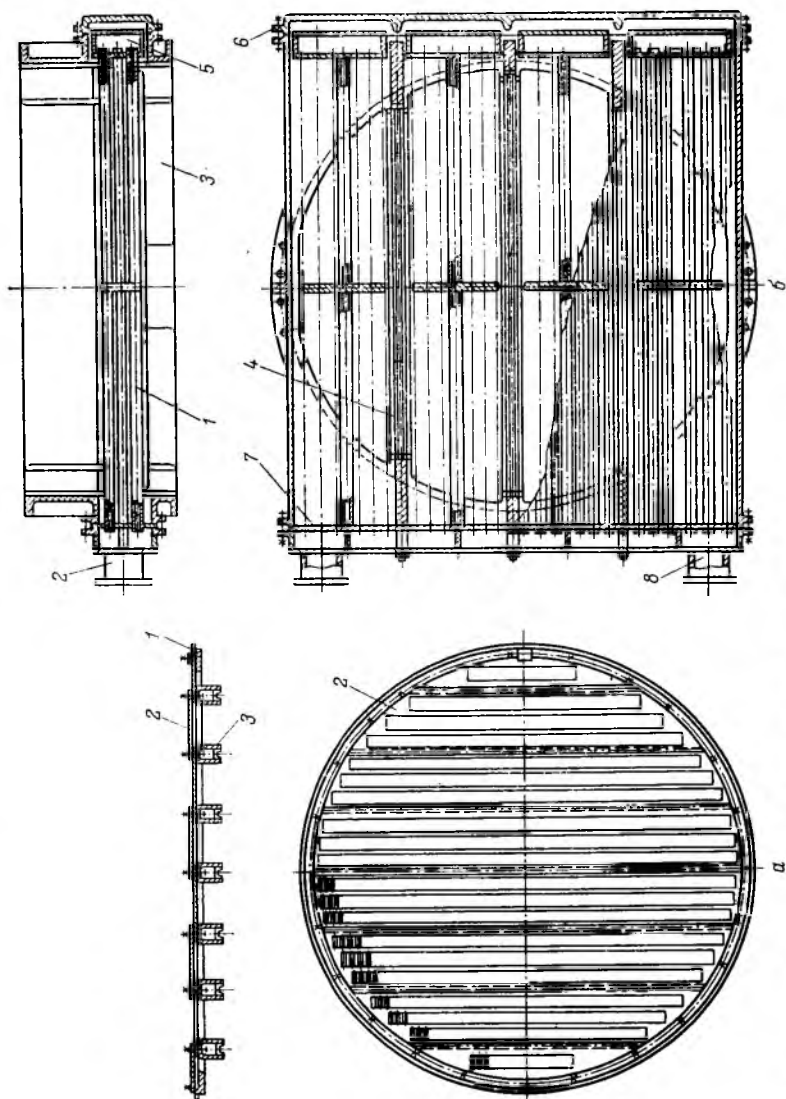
Трубно-решетчатый прогивогочный контактный элемент:
